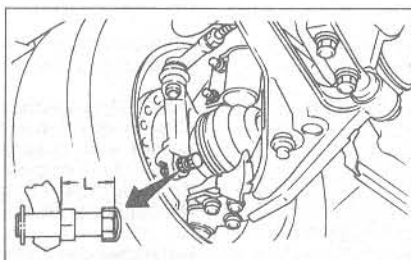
Основные установочные величины стопорного болта угла поворота передних колес (Глава 36)
